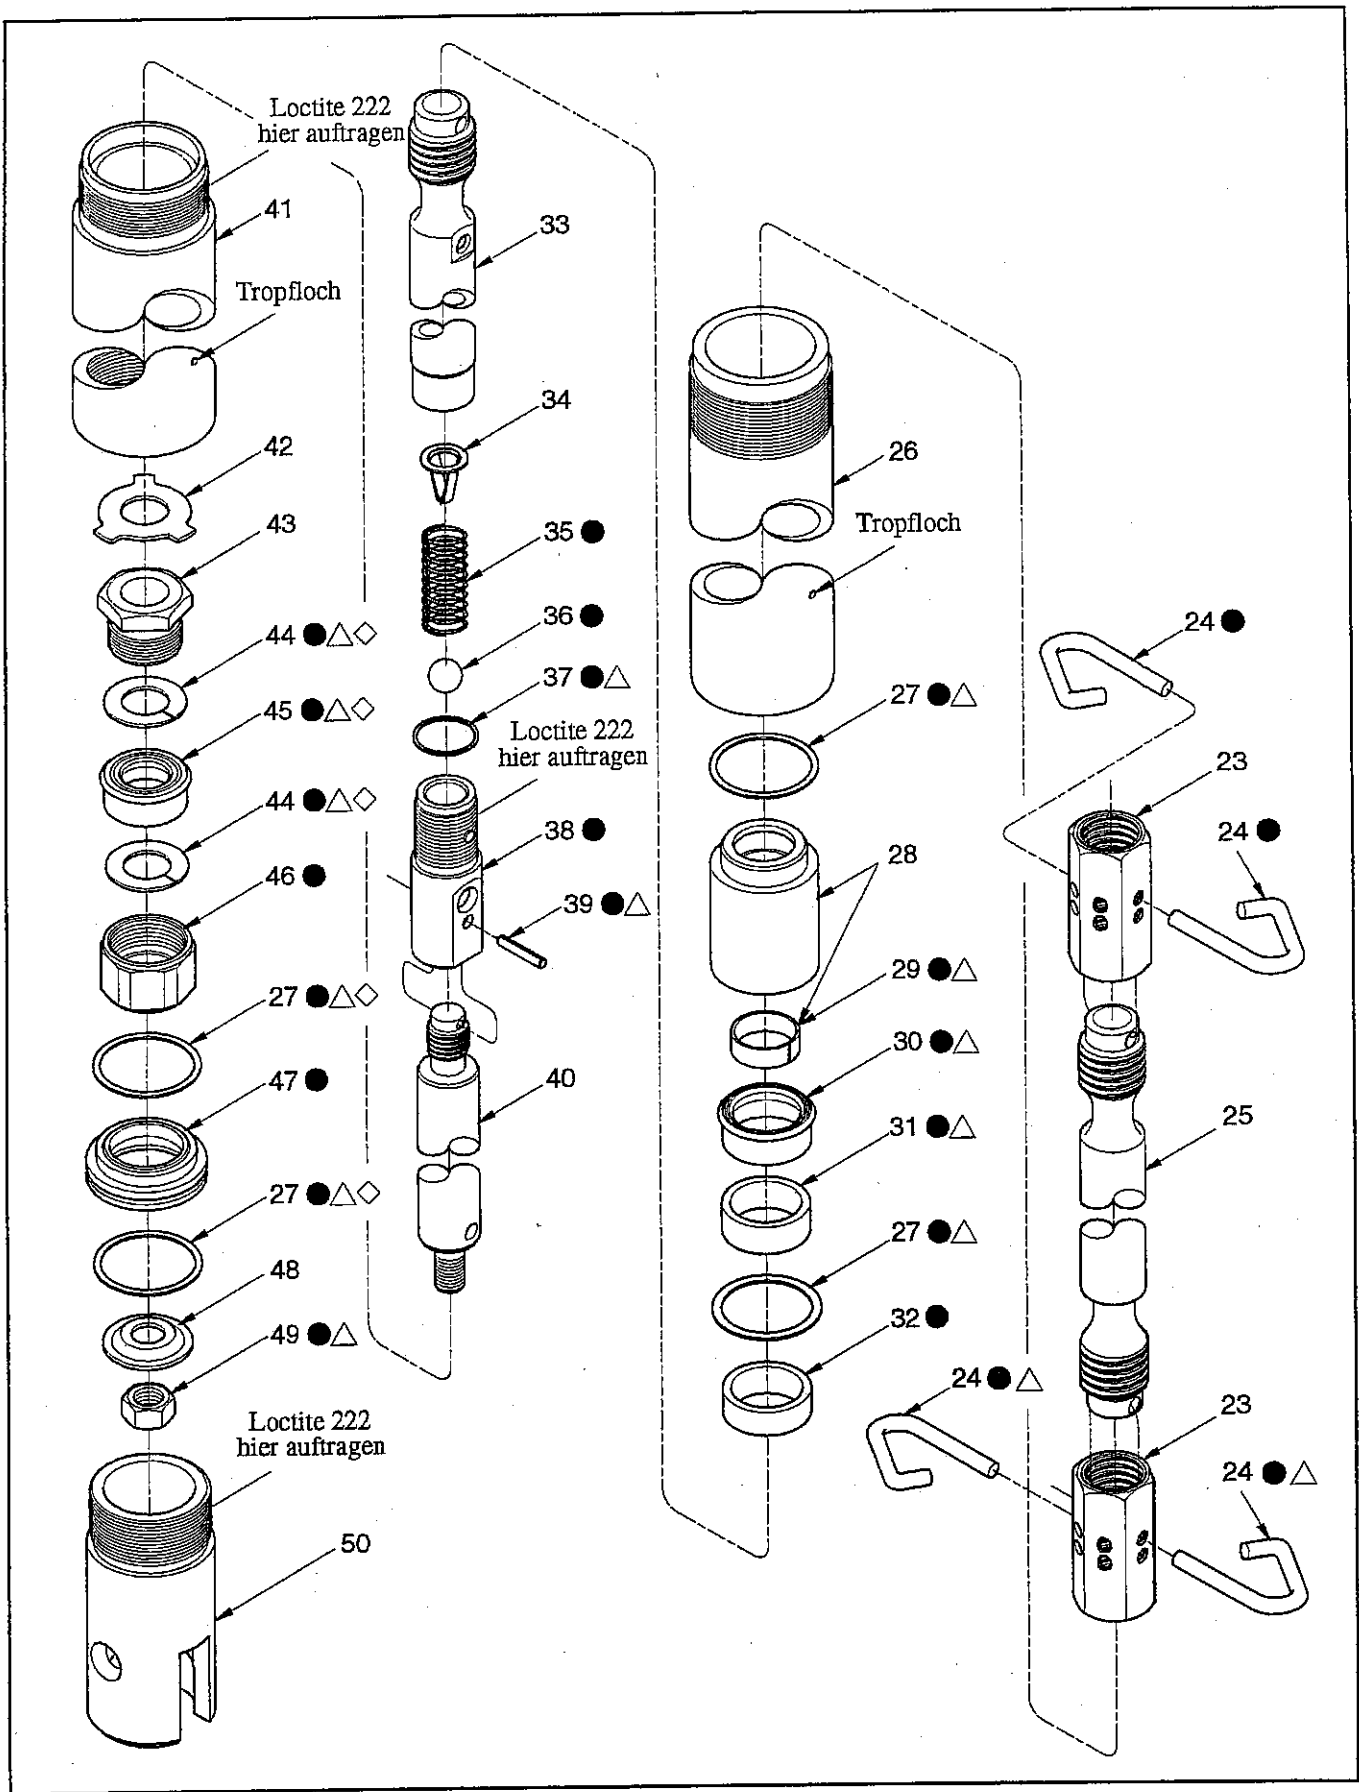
B Hochdruck-Schmierpumpe, Modellreihe 7785 - Explosionszeichnung
